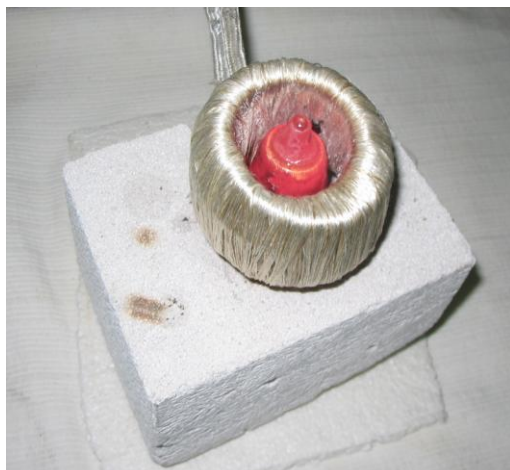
Загальний вигляд індуктора з твердосплавним різцем при нагріванні різця в лабораторній установці ТВЧ
